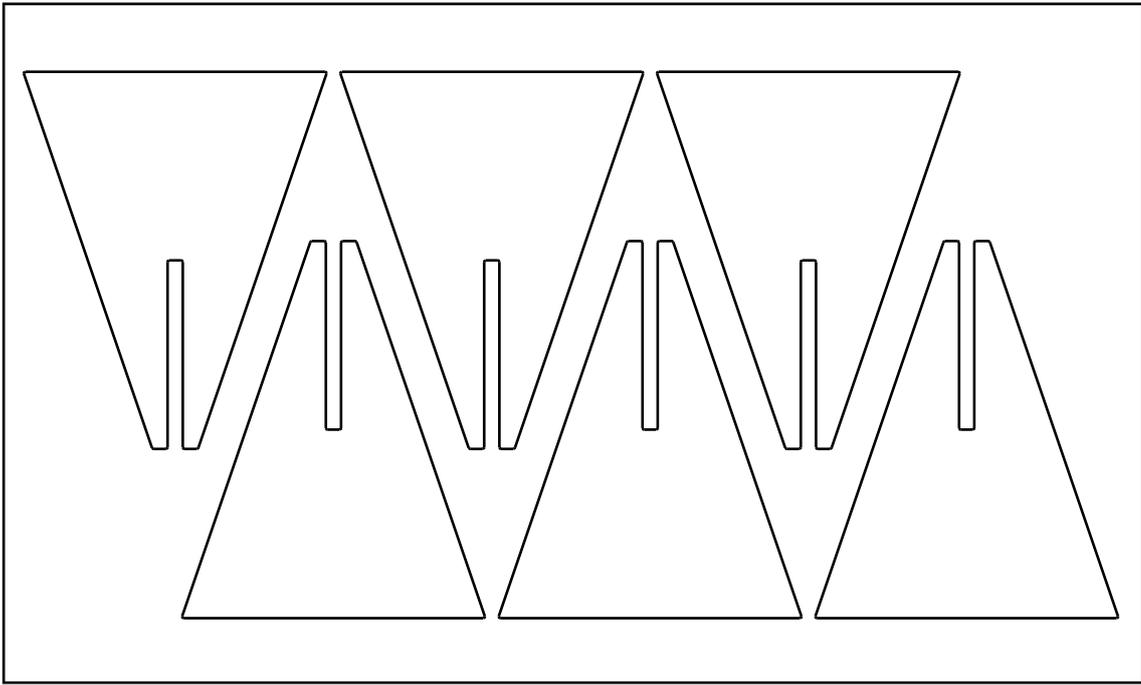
Panel piezas apoyo. Escala 1:10
